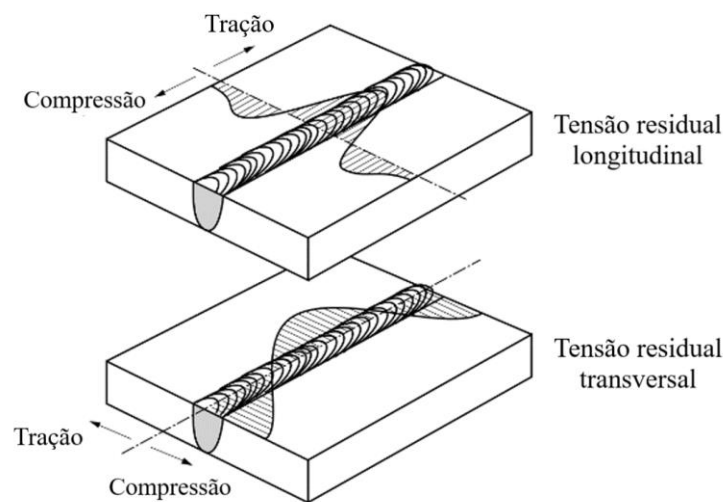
Tensões residuais longitudinais (L) e transversais (T) em uma junta de topo [25]
